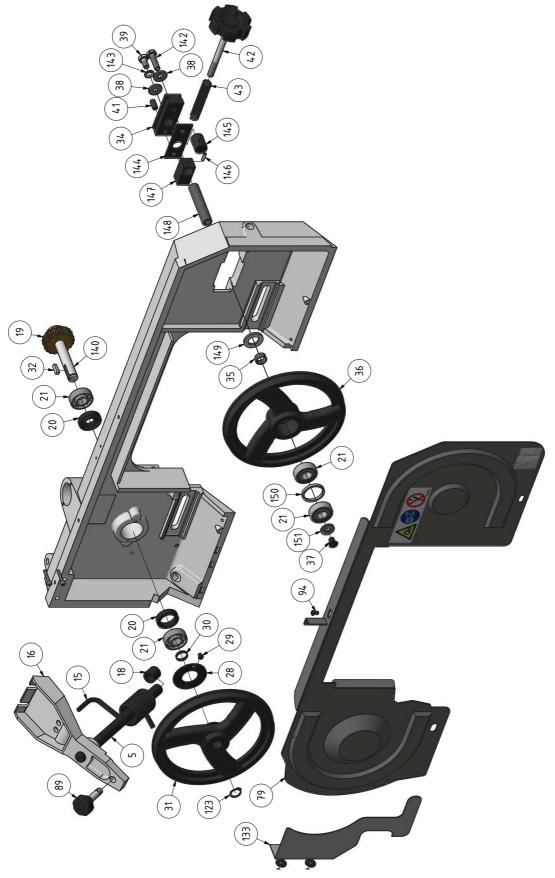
Ersatzteilzeichnung 2 von 4 - Parts drawing 2 of 4
